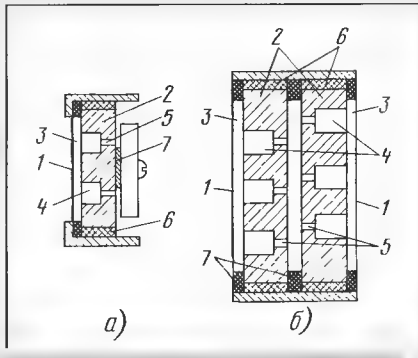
а — одномембранный микрофон; б — двухмембранный микрофон; 1 — мембрана; 2 — неподвижный электрод; 3 — воздушный зазор; 4—5 — отверстия акустических каналов; 6 — изолирующее кольцо; 7 — калиброванные прокладки
